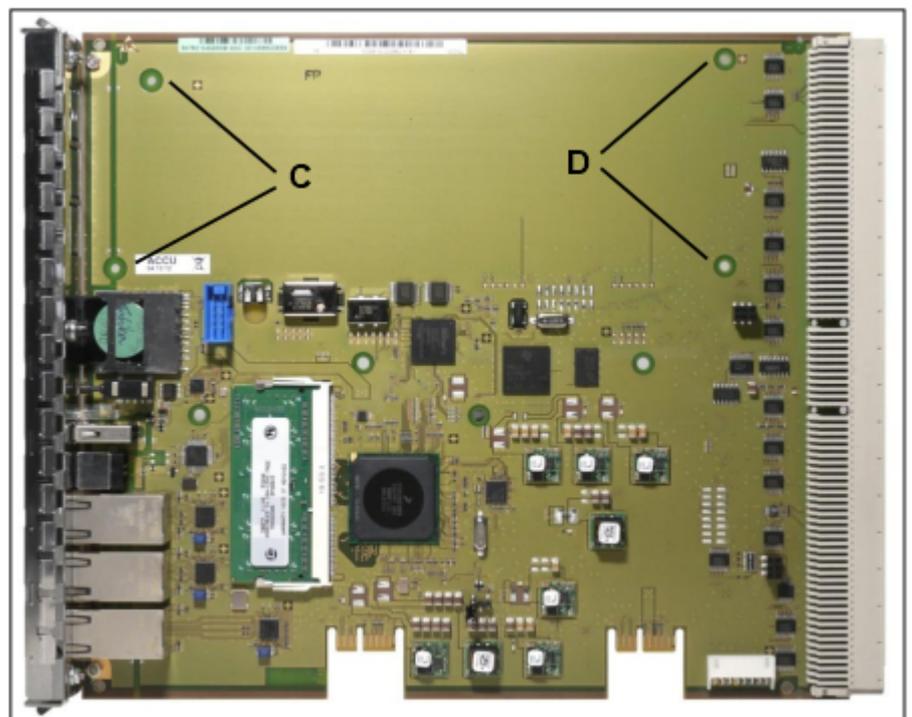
OCCL – Befestigungslöcher für UC Booster Card OCAB
